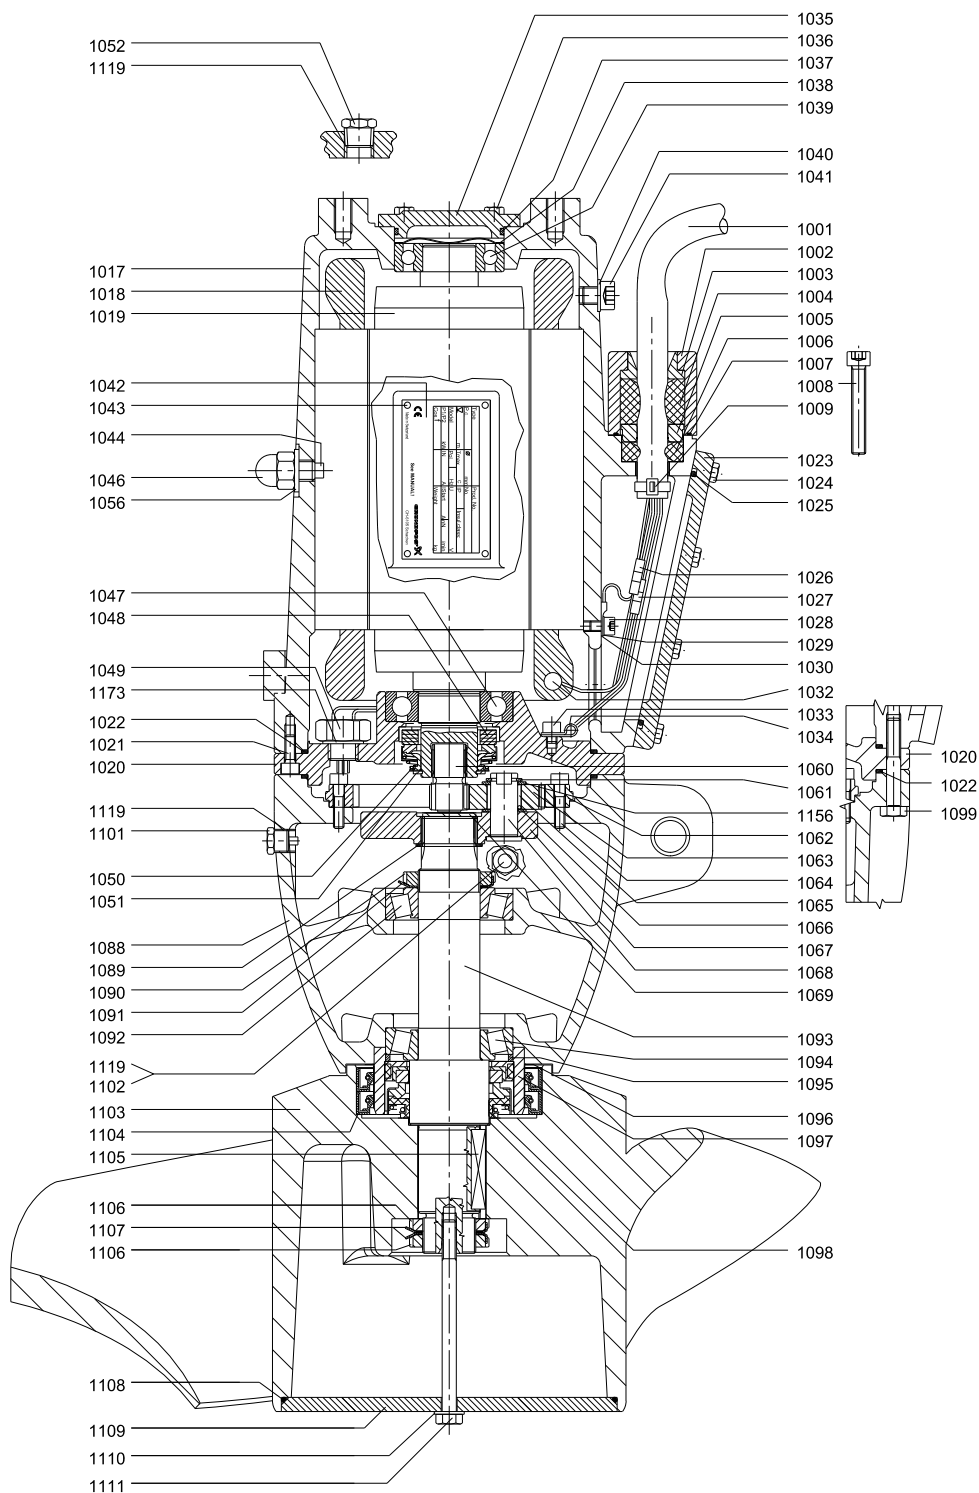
Чертёж в разрезе, SRP.35.50.xxx, SRP.50.50.xxx
